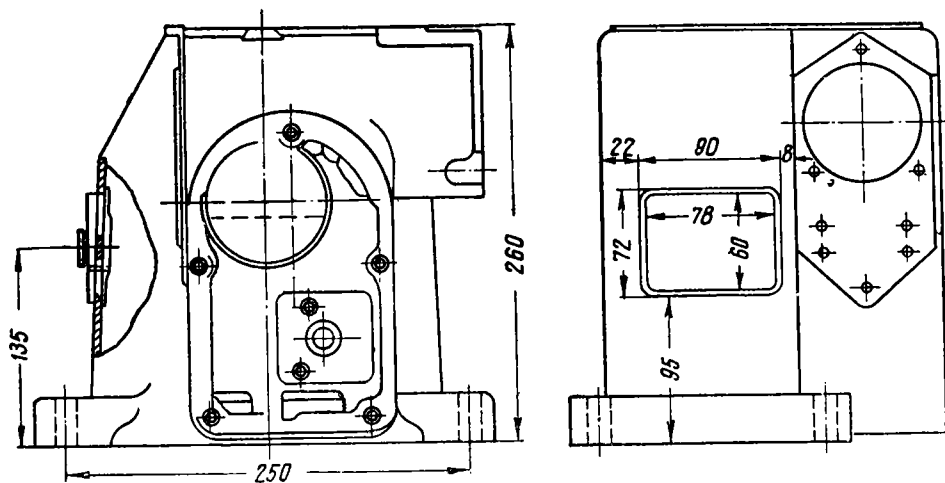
Общий вид картера двигателя Л-3/2 с окном для смотрового люка
